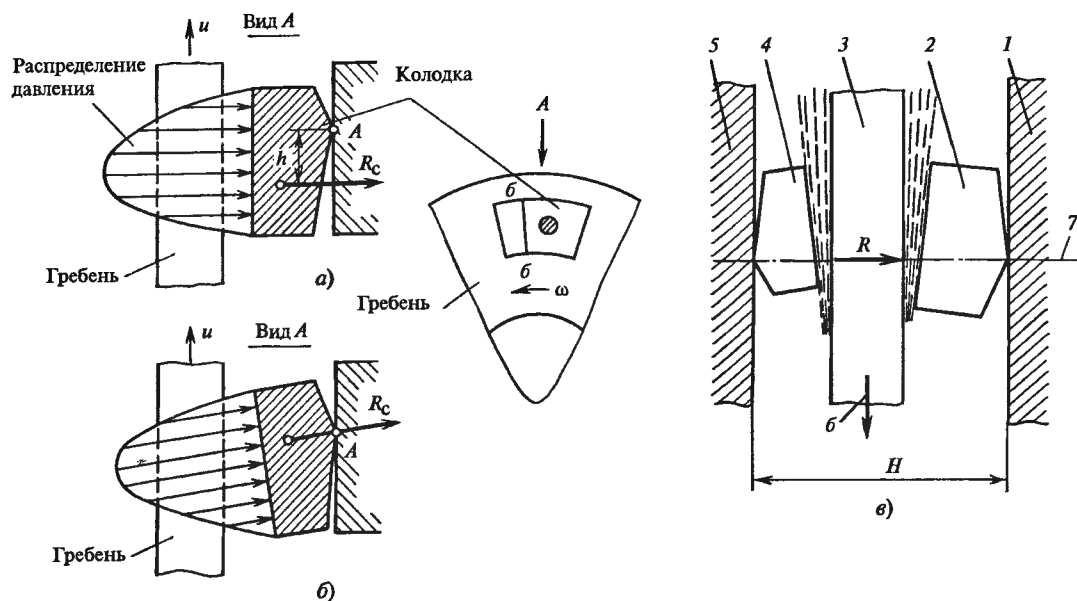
Положения гребня упорного подшипника между упорными колодками:
